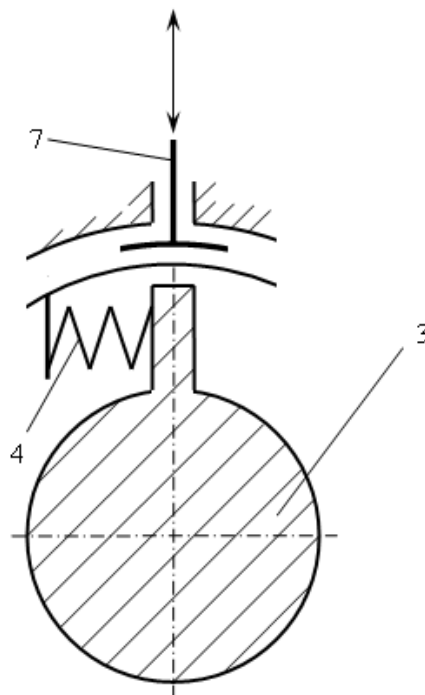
Схема отключения корпуса от промежуточного вала
